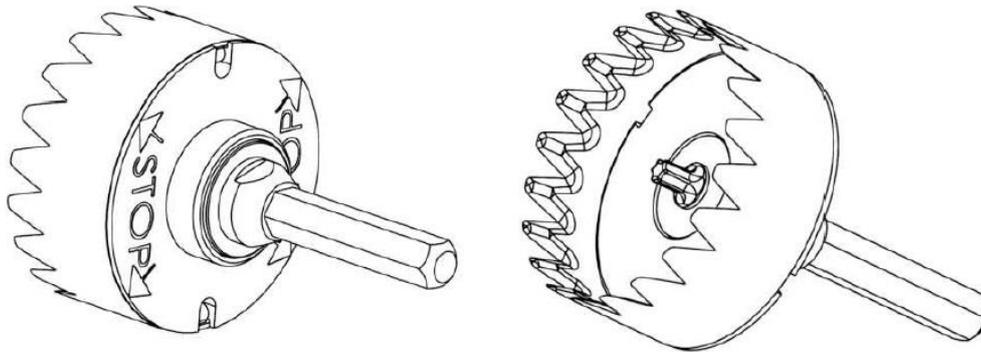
Montagewerkzeug für "BRAVOLL PTH-S"
